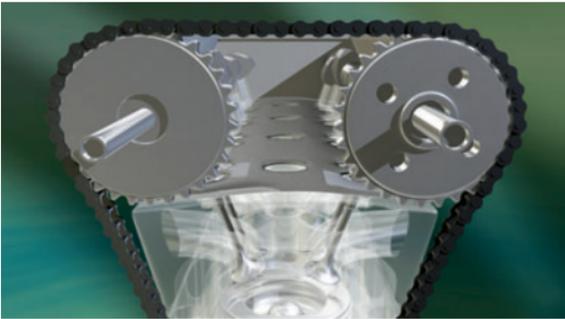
Zylinderkopf mit Steuerkette, Steuer-
